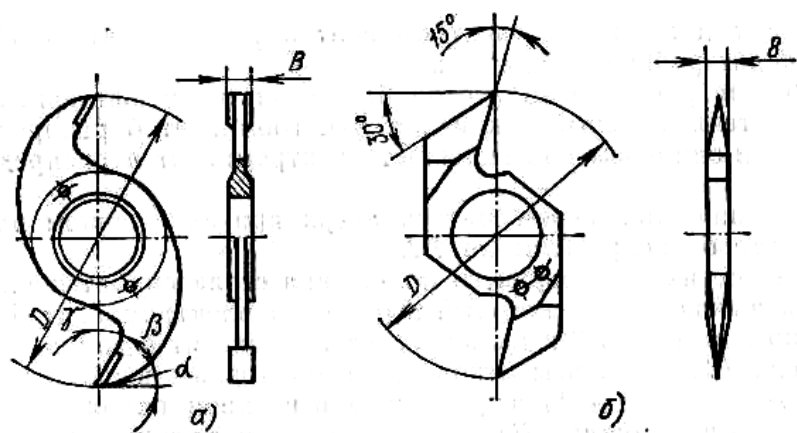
Фреза для обработки ящичных шипов прямых (*а*) и клиновых (*б*)
